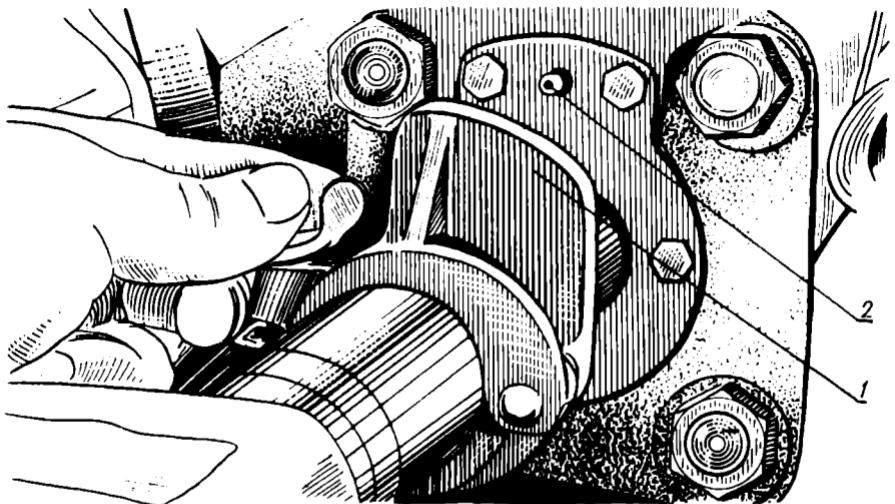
Регулирование хода поршня цилиндра подвижным упором:
